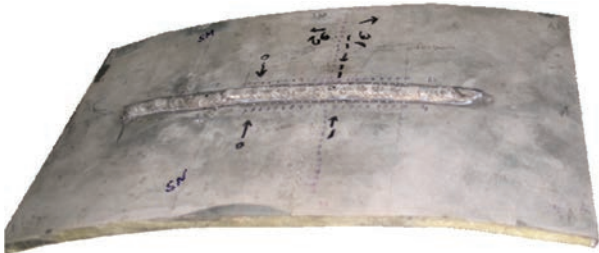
Образец ремонтного сварного соединения из магниевого сплава МЛ10
